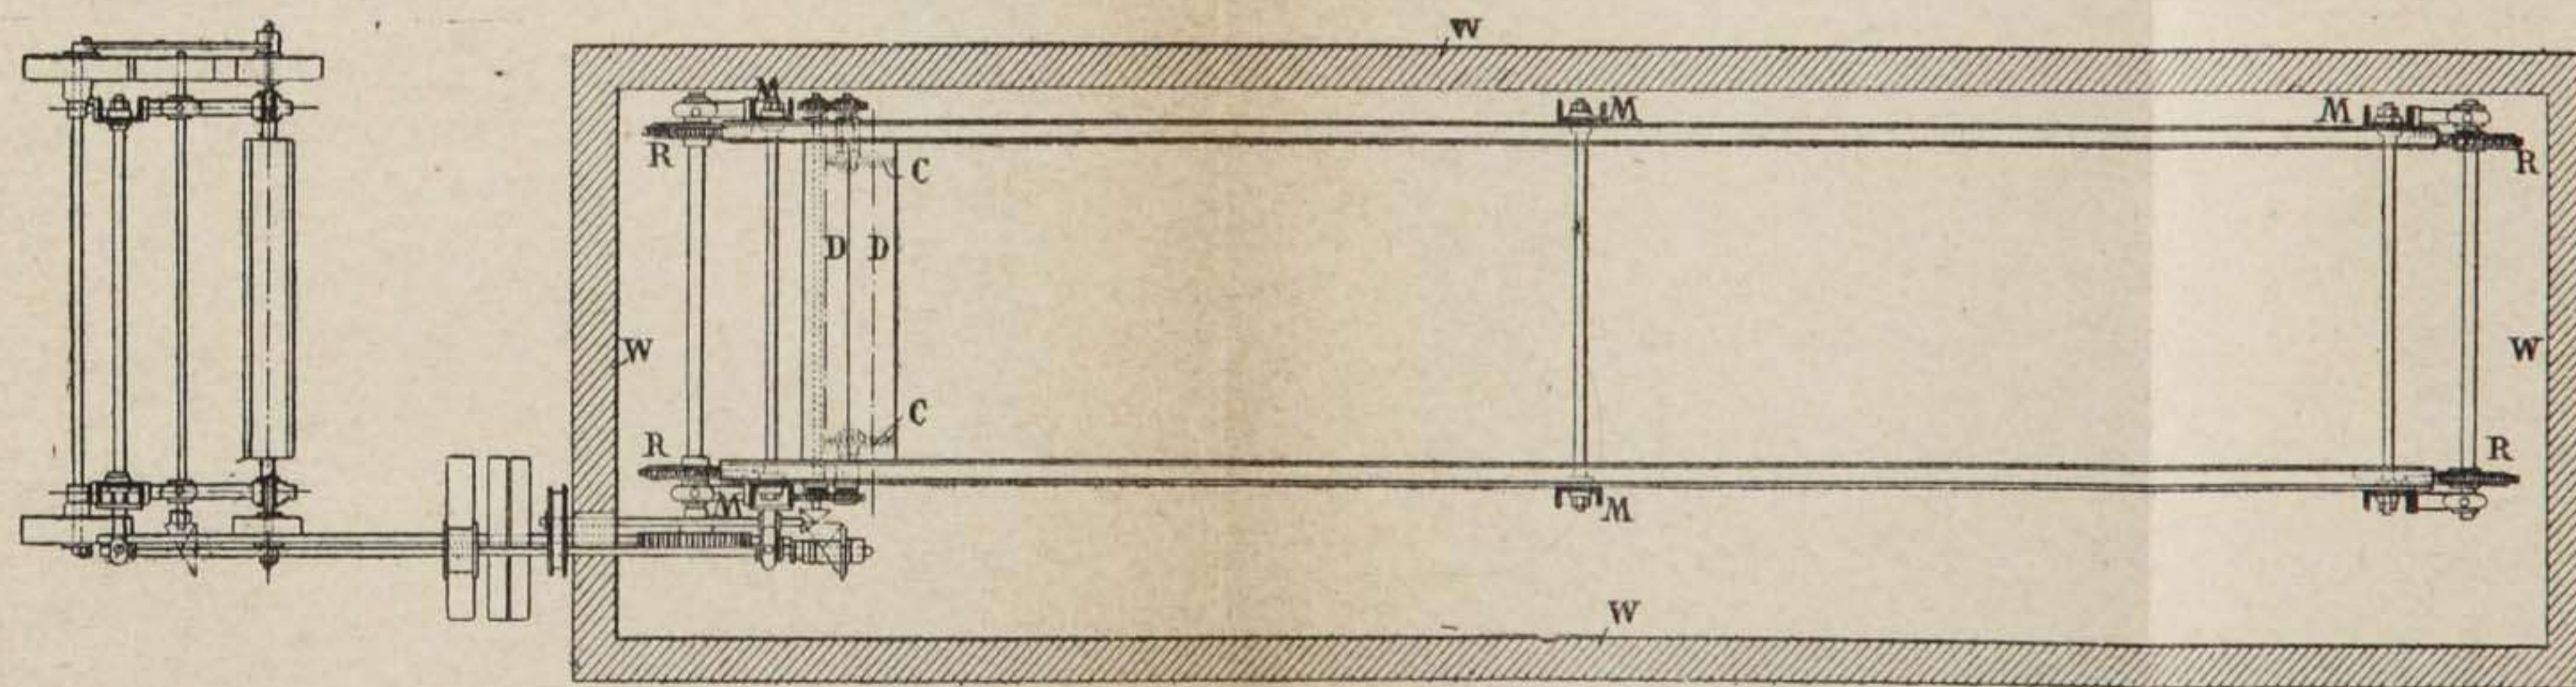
Machine à vaporiser système continu REMY. — Plan.
